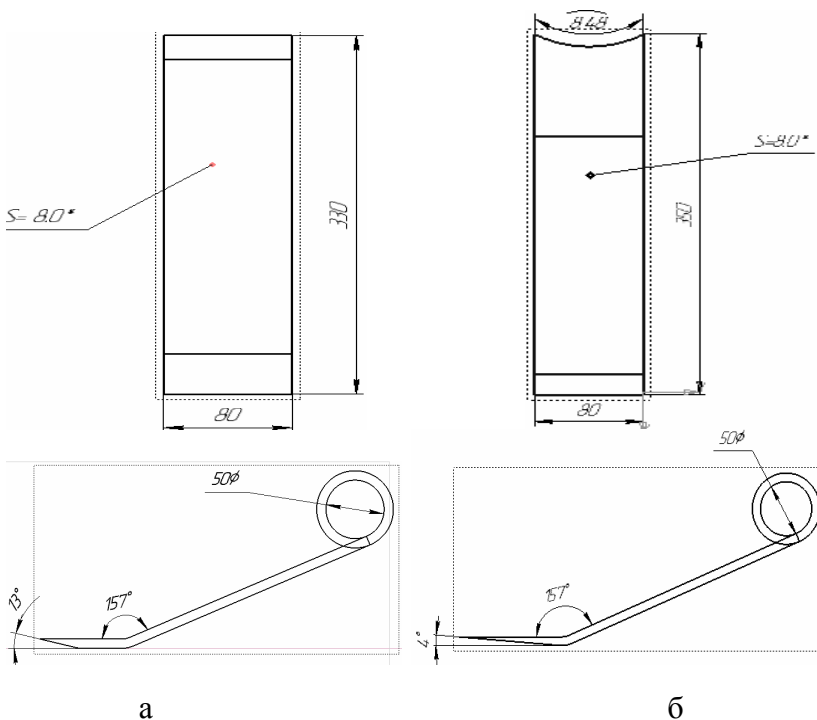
Размеры исходного ножа (а) и предлагаемая конструкция ножа (б)
